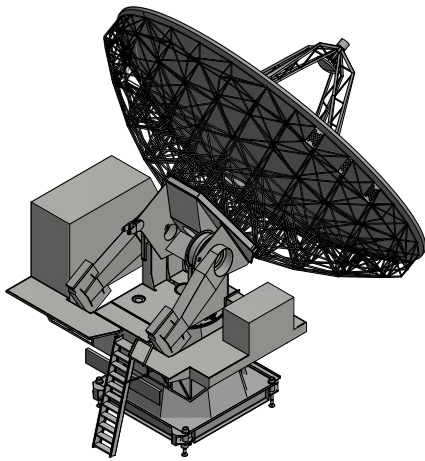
Vista isométrica parte trasera. [35] Figura 3.26: Vista isométrica parte frontal. [35]
